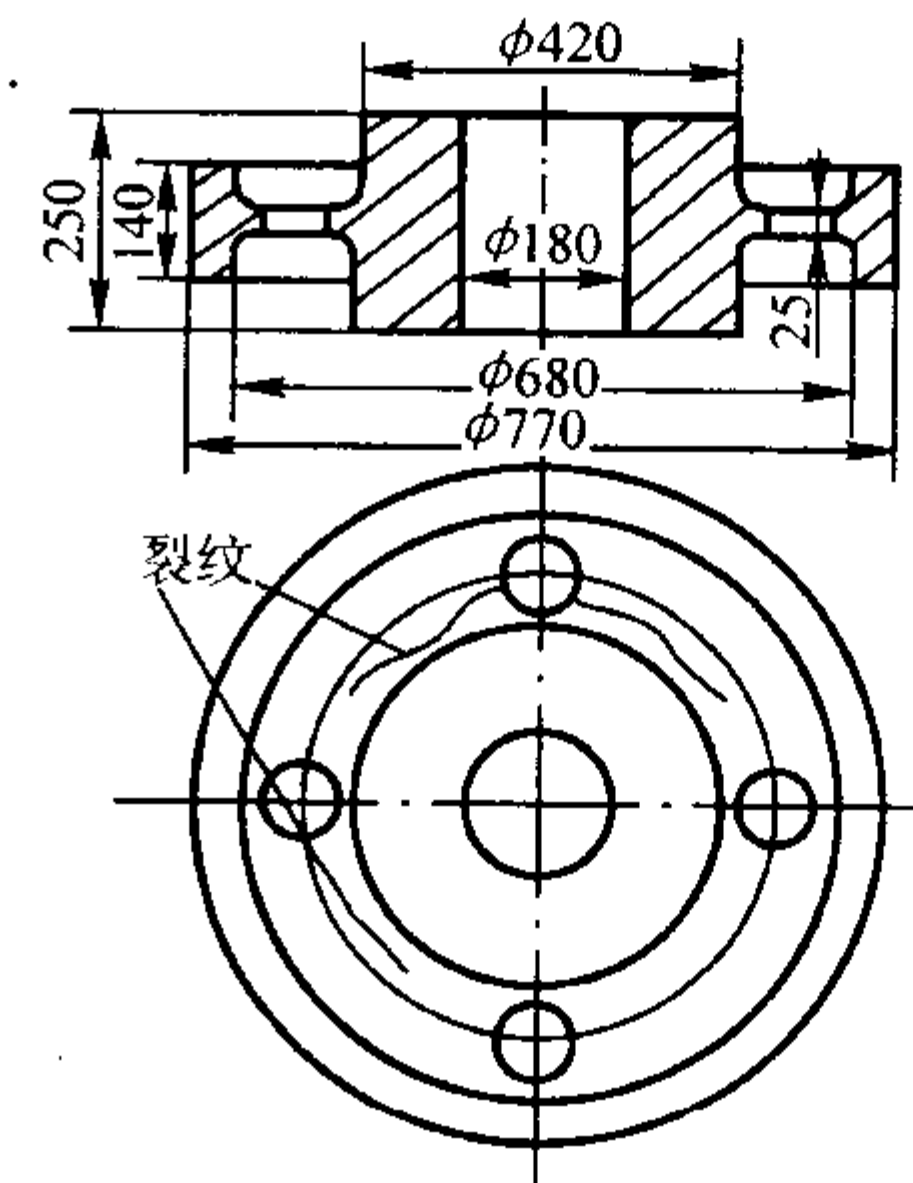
ZG35CrMn 齿轮毛坯的冷裂纹
